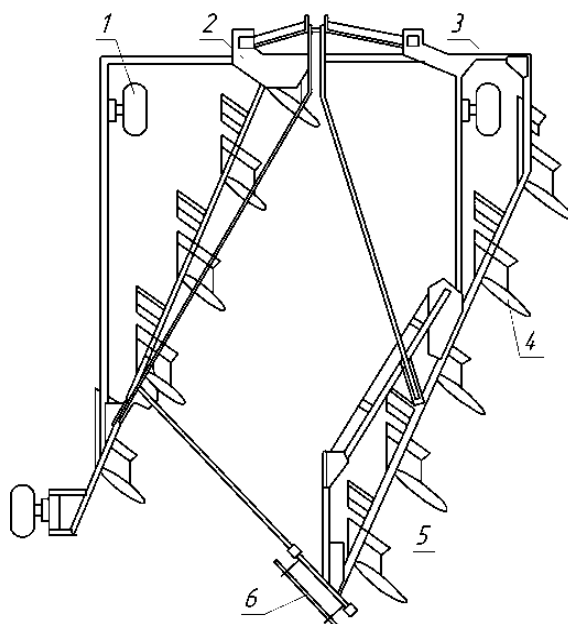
Двухрядный навесной секционный плуг ПСН-10-35: 1 – опорные колеса; 2 – механизм навески; 3 – рама; 4 – отвальные корпуса; 5 – предплужники; 6 – заравниватели
